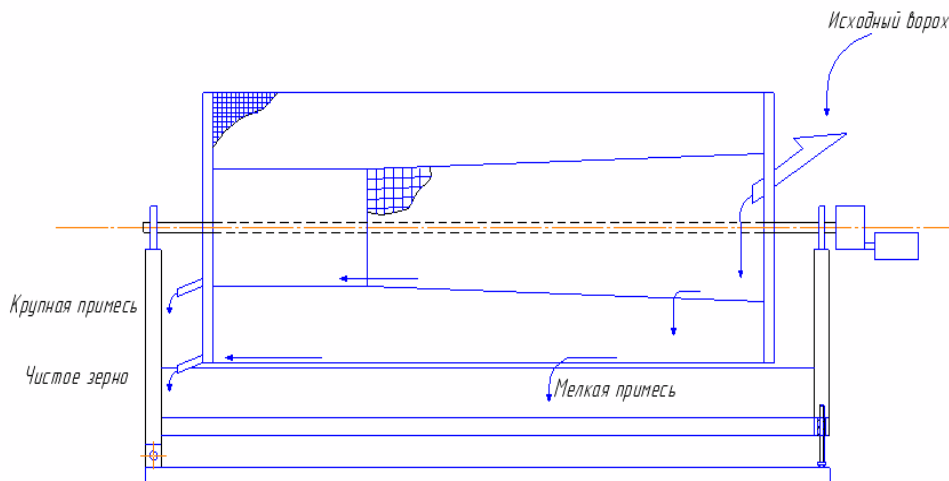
Конструктивно-технологическая схема со сдвоенными цилиндрическими решетами
